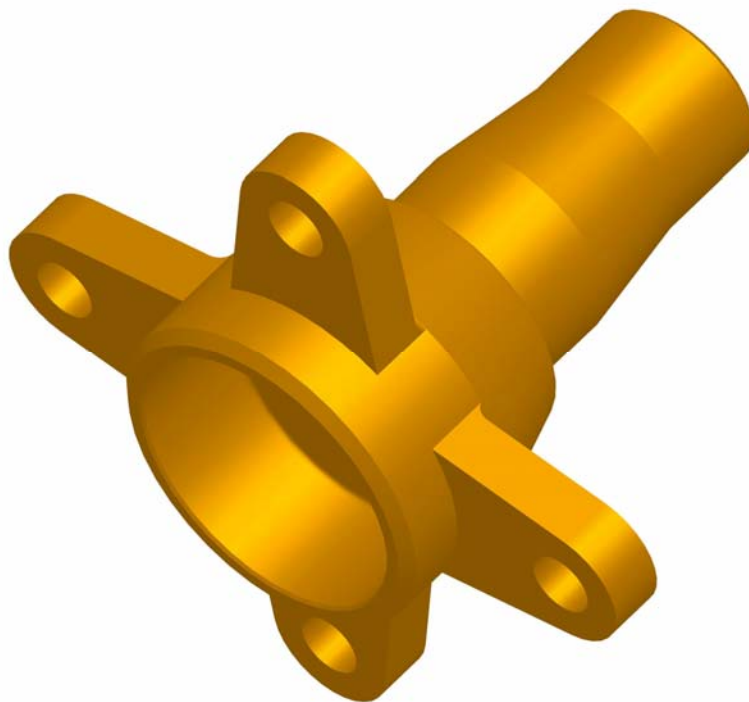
Konstrukční řešení horního segmentu zadní těhlice
